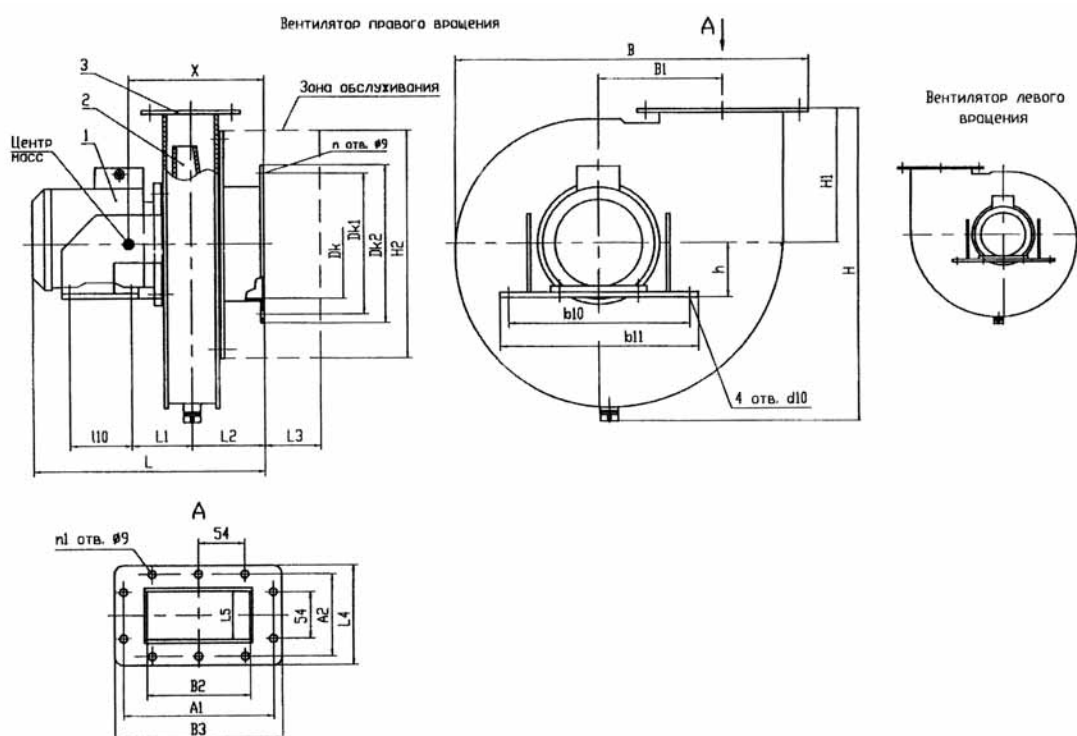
1 – двигатель; 2 – колесо рабочее; 3 – корпус
